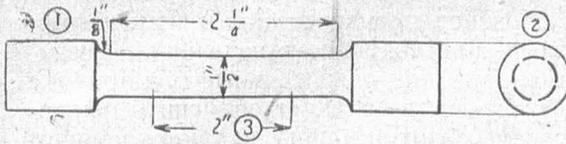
Образец из наплавленного металла для испытания на разрыв. 1 — радиус закругления не менее  $1/8$ "; 2 — обработка по всей поверхности; 3 — длина средней части и переход к более толстым концам должны быть такими, как указано на рисунке; концы образца могут быть произвольной формы, которая могла бы быть закреплена в разрывной машине
